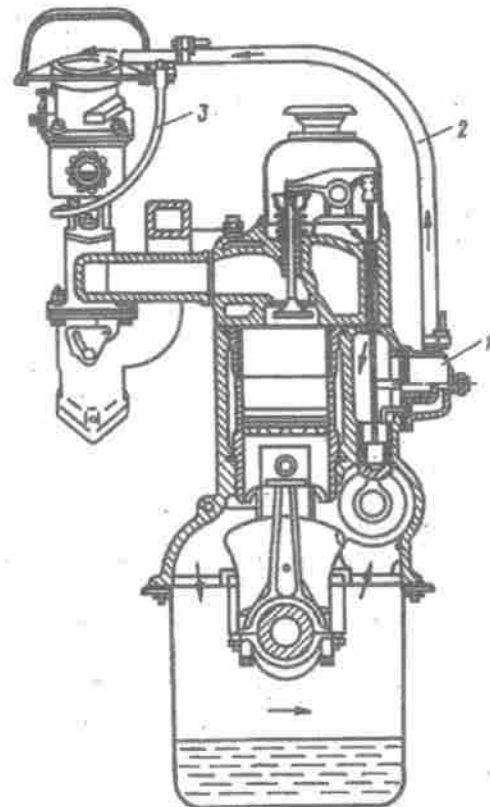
Belüftungssystem des Kurbelgehäuses des Motors:
